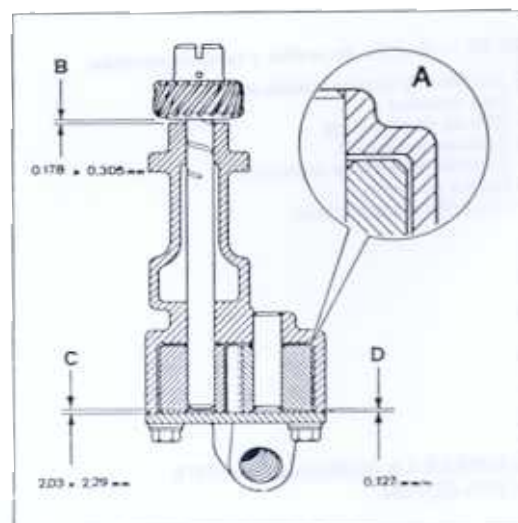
A-Z2C-01 — Dimensiones y detalle de montaje de los engranajes de la bomba de aceite.
